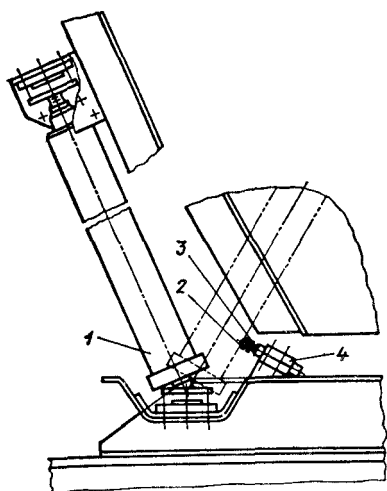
Установка гидроцилиндра и ограничительного клапана при расположении гидроцилиндра перед платформой
